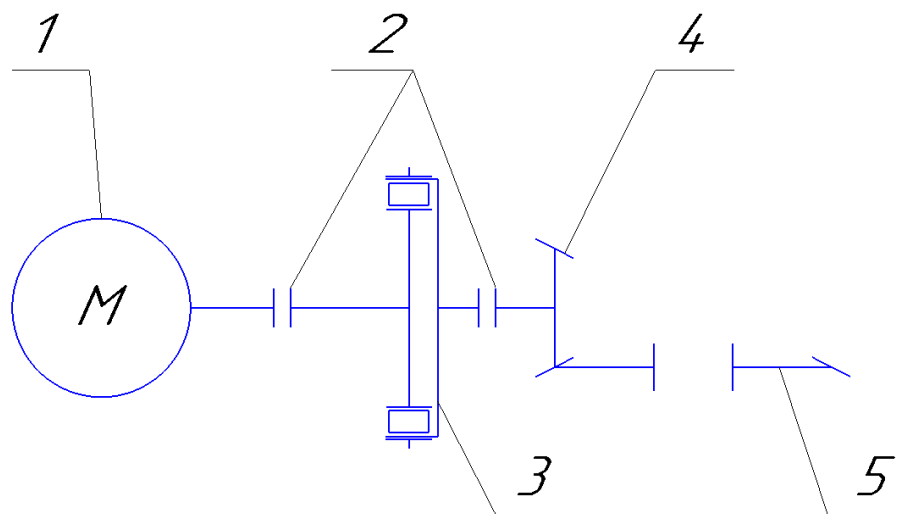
Кинематическая схема резьбонарезной РМ с ВППТК
